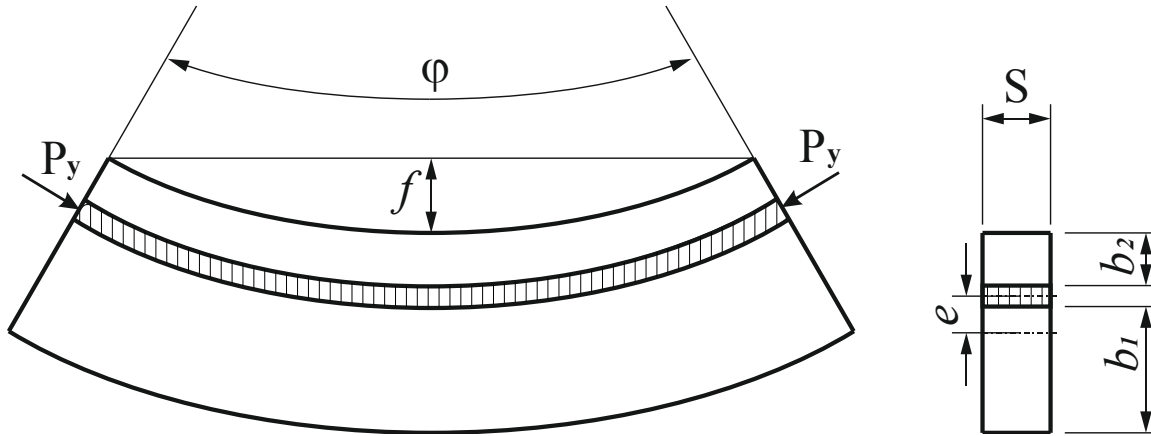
Схема изгиба пластин под действием усадочной силы
